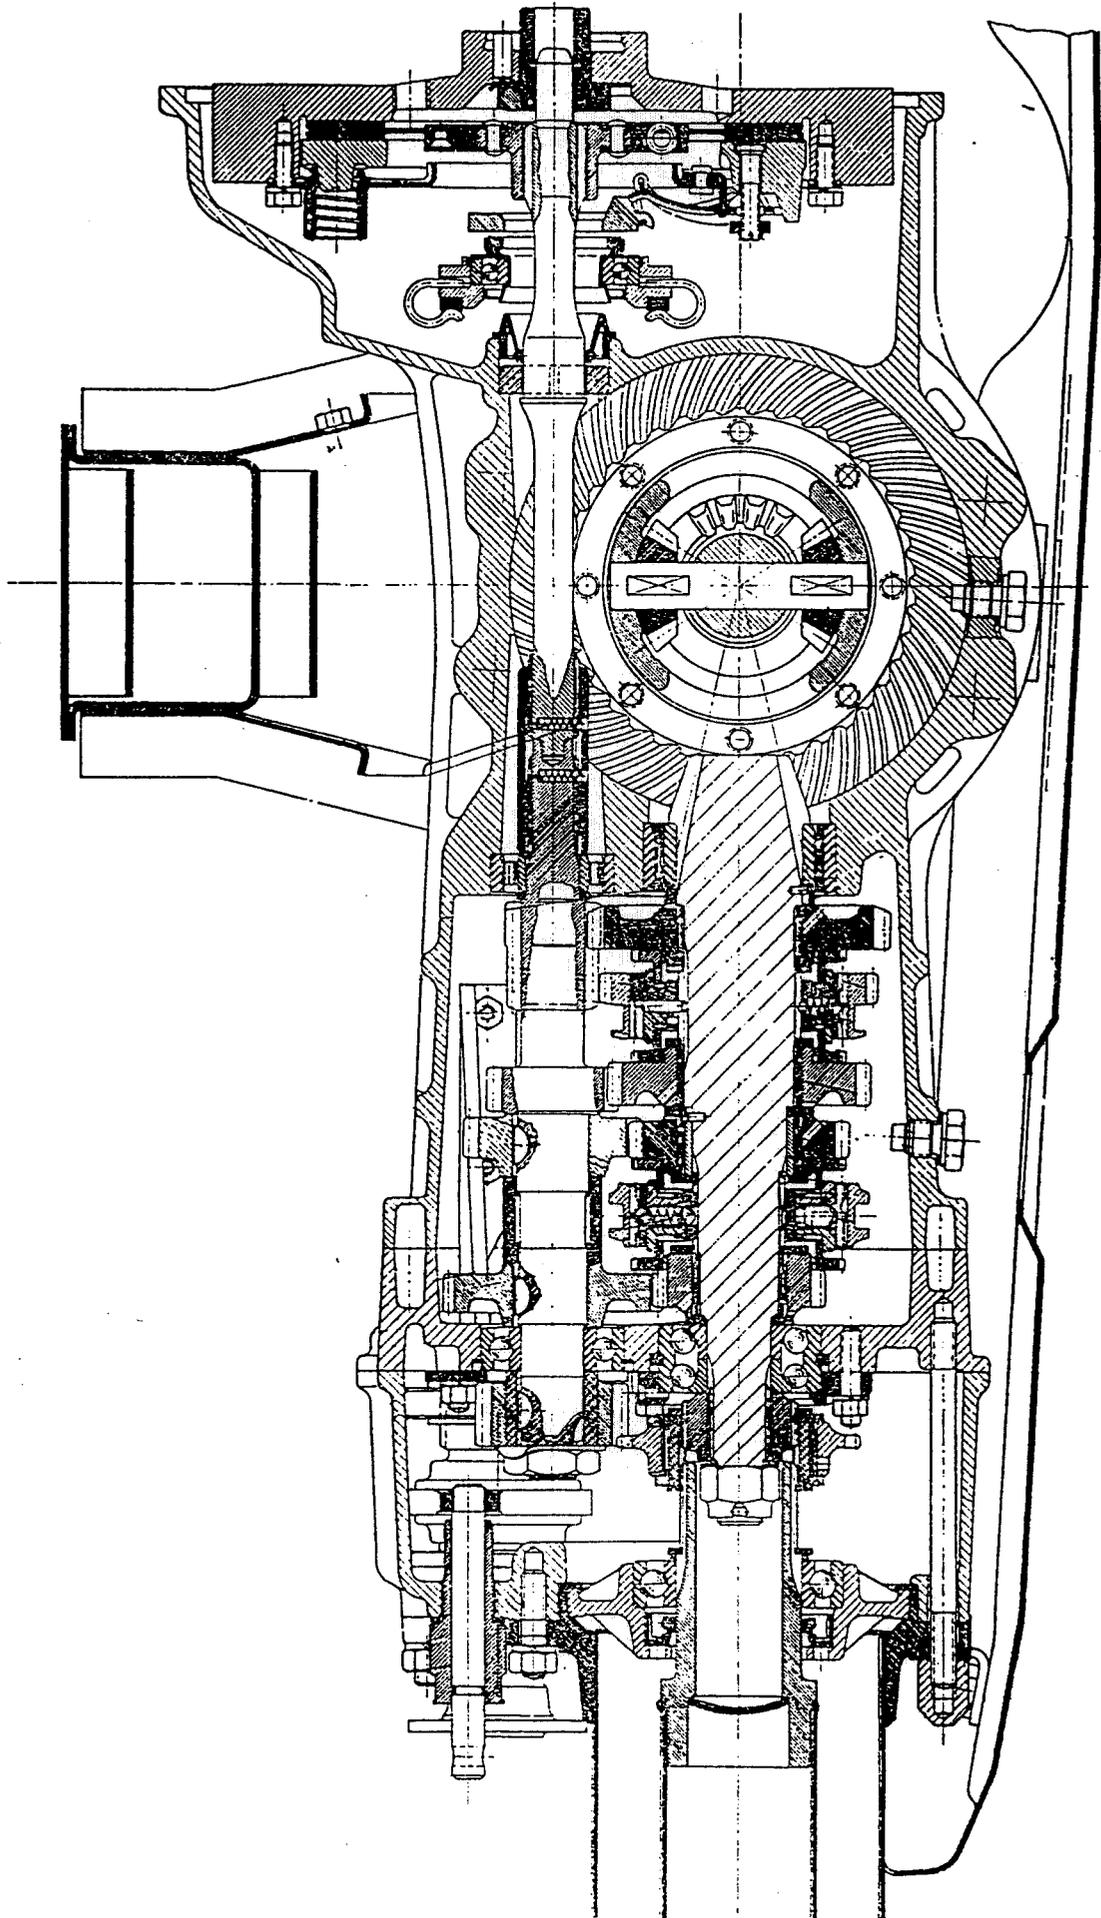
/I: Getriebe - Gear - Engrenage de transmission
